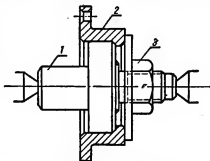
Гладкая оправка с креплением обрабатываемой детали гайкой:
